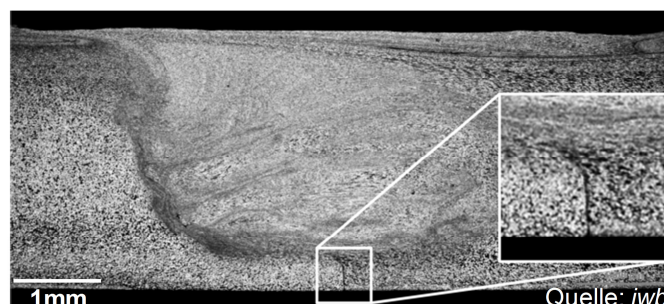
Bildung einer offenen Schweißnahtwurzel /AiF09/
